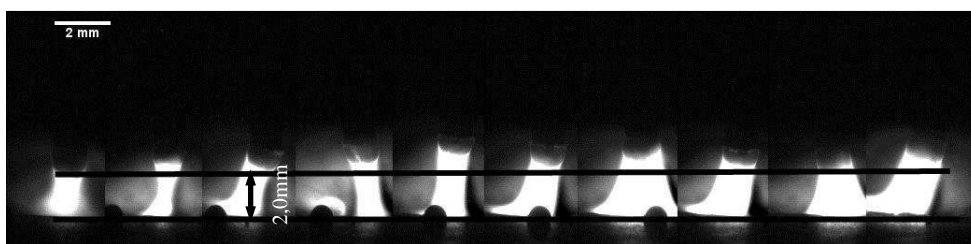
Medição do comprimento do arco em 10 diferentes momentos da soldagem com tensão de base de 21V (2,0 mm)
